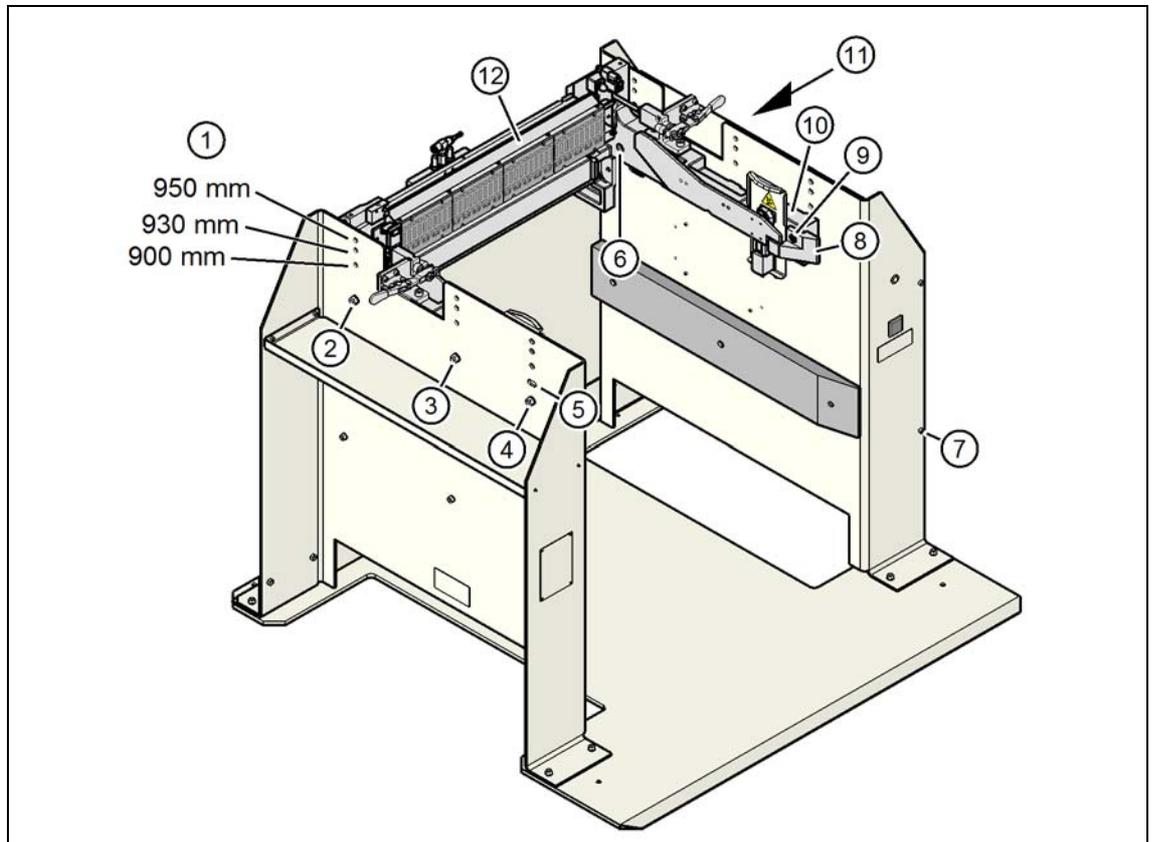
将料车装卸装置调整为 PCB 传送导轨高度
